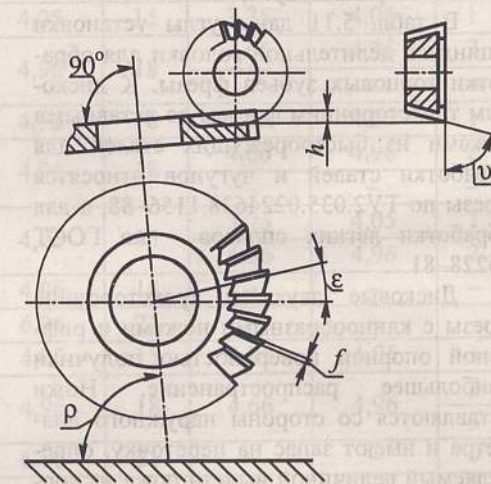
Схема фрезерования торцевых зубьев дисковой фрезой
